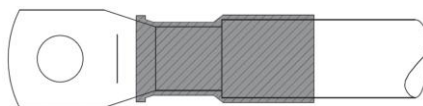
Пример применения термоизоляционной трубки (выделена штриховкой) для изоляции соединения кабельного наконечника и силового кабеля
